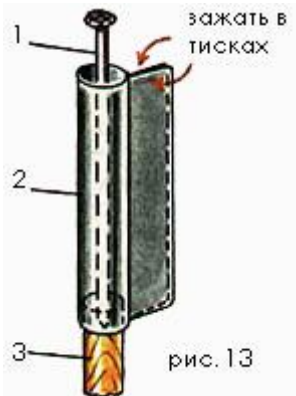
Изготовление корпуса девона методом литья; 1 - гвоздь; 2 - оболочка из фольги; 3 - деревянный стержень
